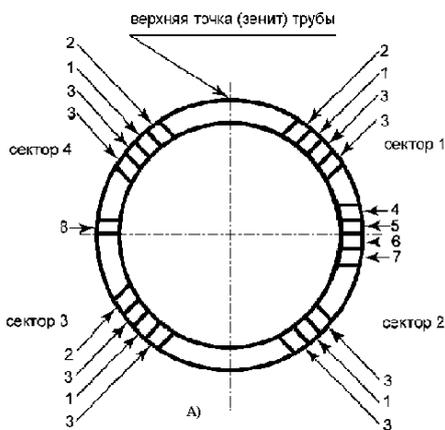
Схема вырезки темплетов для изготовления образцов для проведения механических испытаний сварных соединений труб (диаметром 426 мм и более) в процессе аттестации технологии сварки.
